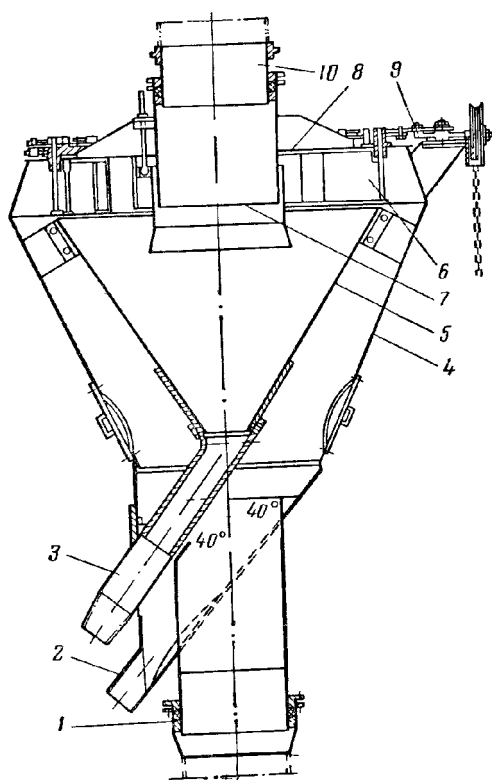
Сепаратор центробежного типа для шаровой барабанной мельницы.
